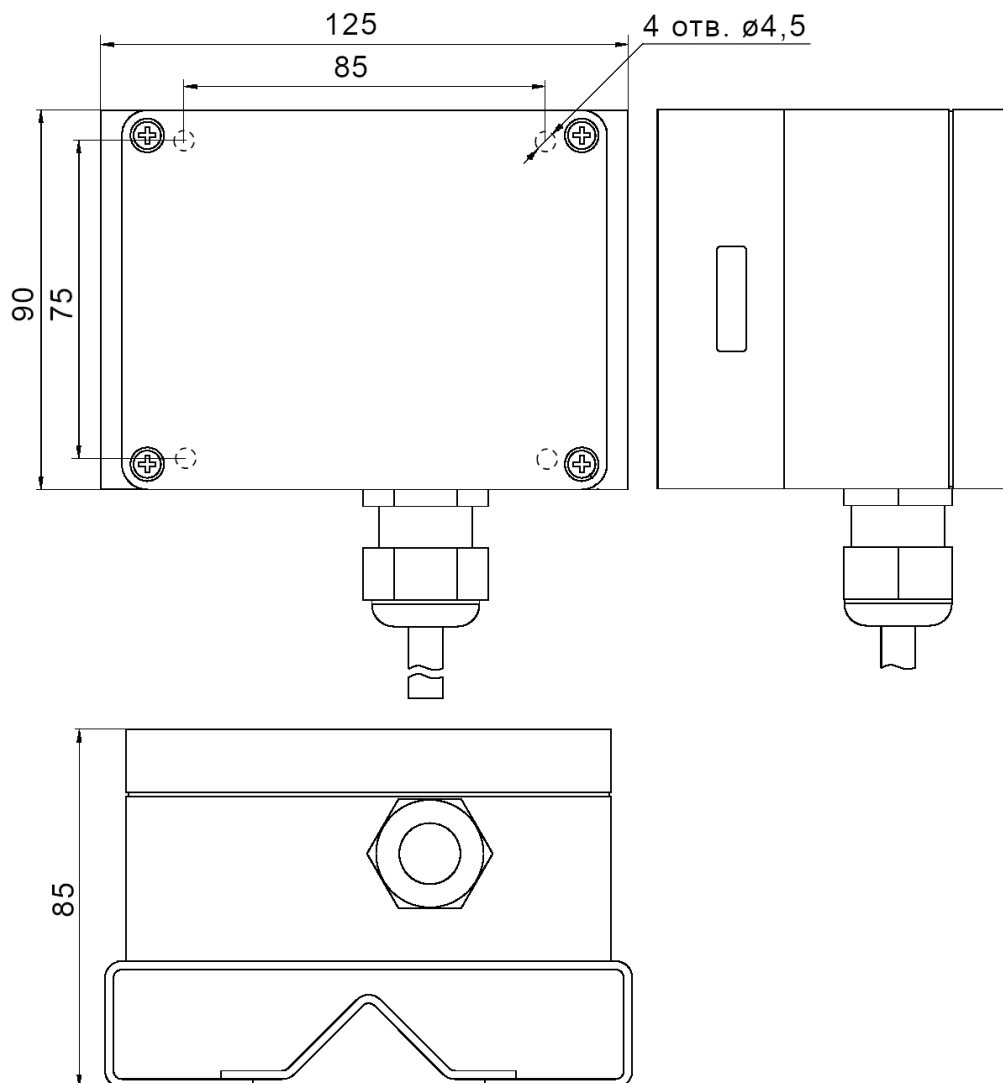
Габаритные и установочные размеры устройства M22.003.00.000-01
